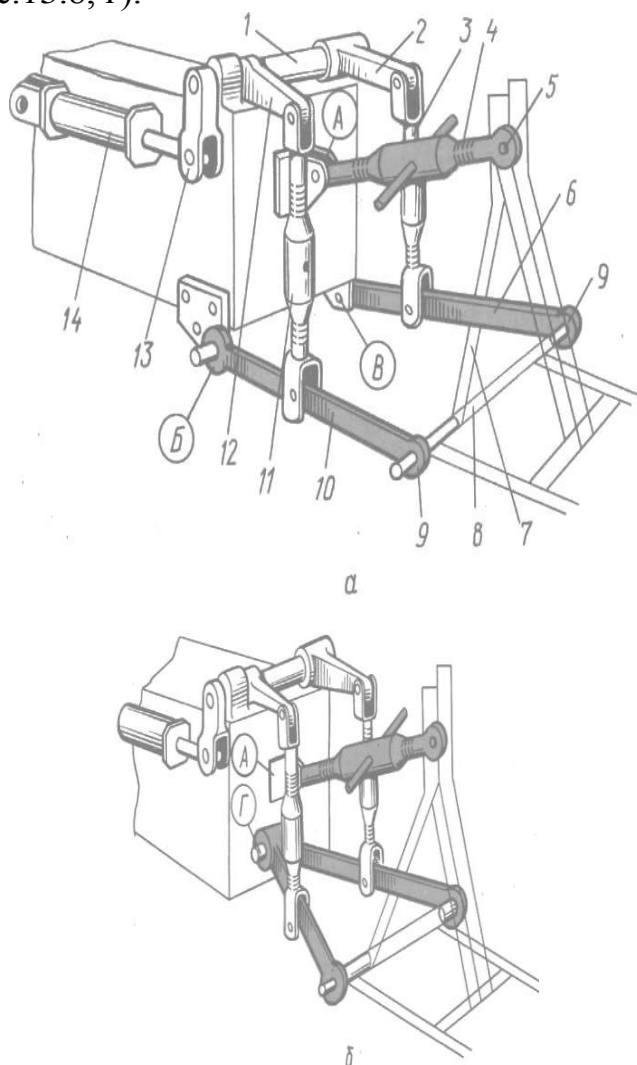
Схемы механизма навески: а - трехточечная; б - двухточечная; 1 - вал подъемных рычагов; 2 и 12 - подъемные рычаги; 3 и 11 - раскосы; 4 - верхняя тяга; 5 - присоединительный шарнир верхней тяги; 6 и 10 - нижние тяги; 7 - стойка навесной машины; 8 - ось подвеса машины; 9 - присоединительный шарнир нижних тяг; 13 - рычаг вала; 14 - гидроцилиндр; А - точки присоединения верхней тяги; Б, В и Г - точки присоединения нижних тяг
